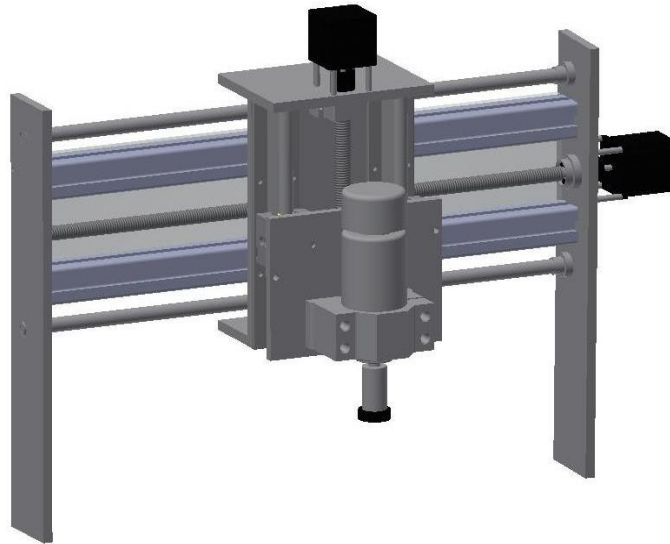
Rám frézky s trapézovým šroubem a krokovým motorem
